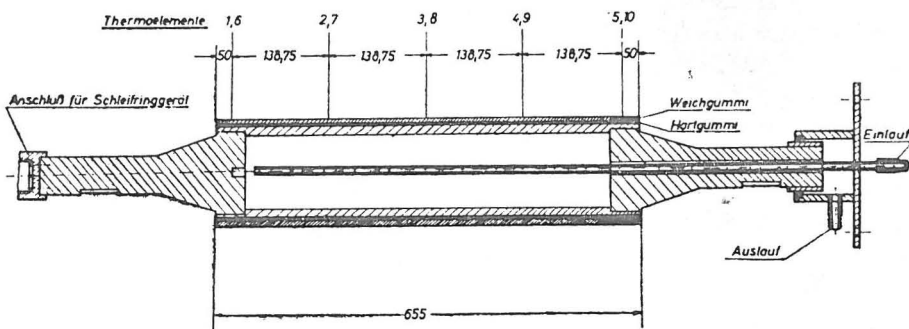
Gummipresseur mit Kühlvorrichtung und Positionsangabe der Meßstellen
